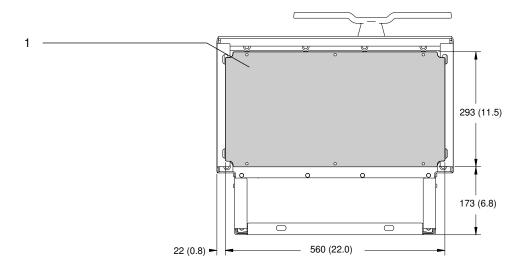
Espace pour la porte et dimensions de la plaque d'entrée des câbles pour E1h
